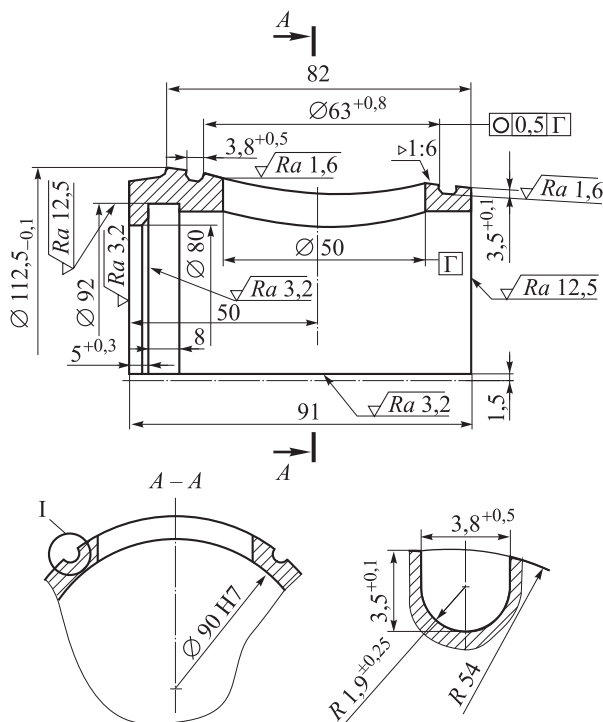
Схема конструкции детали «Вкладыш SK.003»
